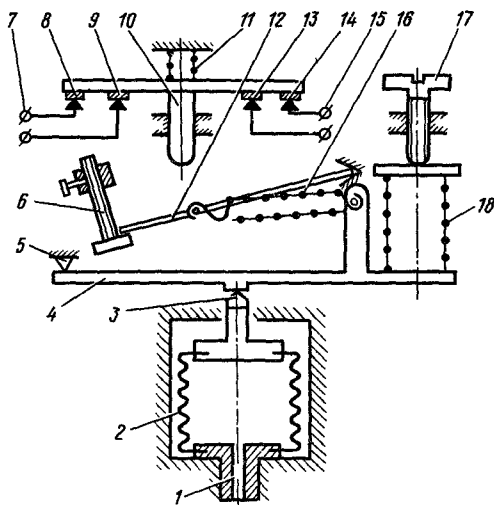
Схема регулятора давления TSP-2В (TSP-11)
